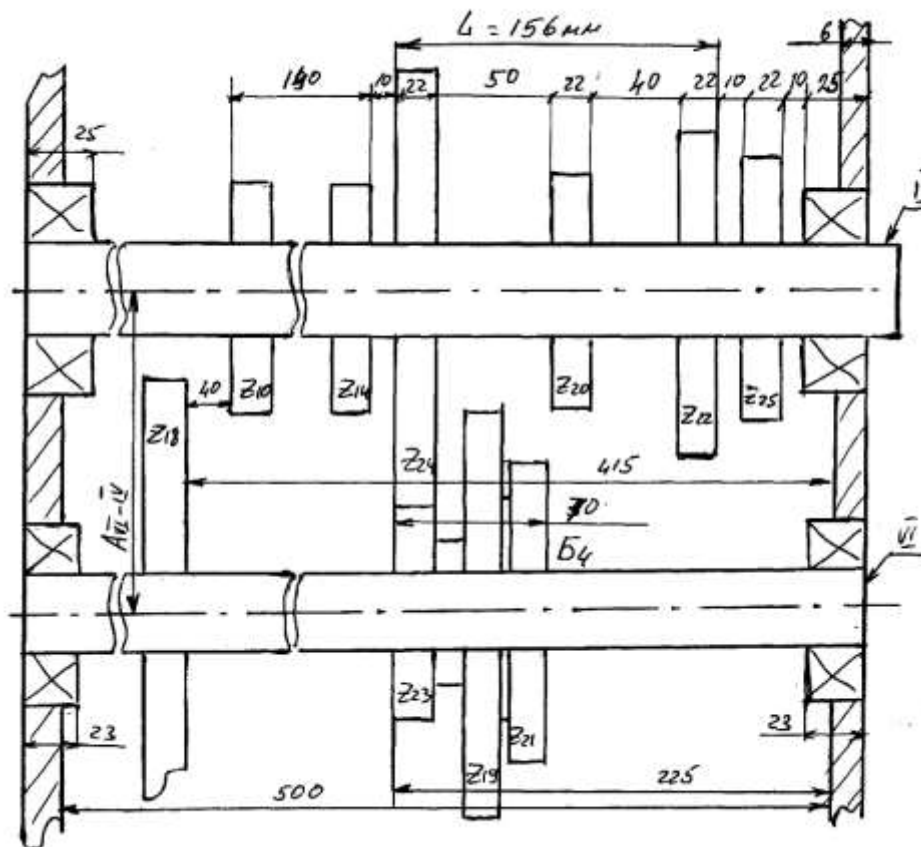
Компоновочная схема развертки наиболее нагруженной группы передач
